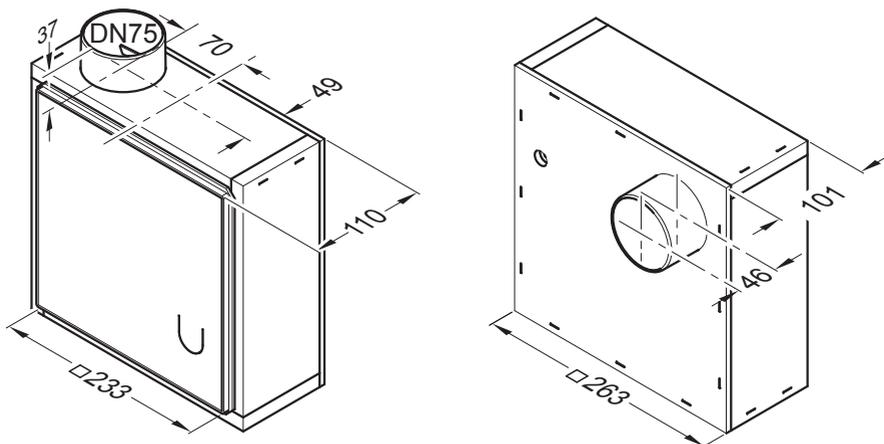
размеры корпуса типов UB, UB-H, UBK и UBK-H в мм
